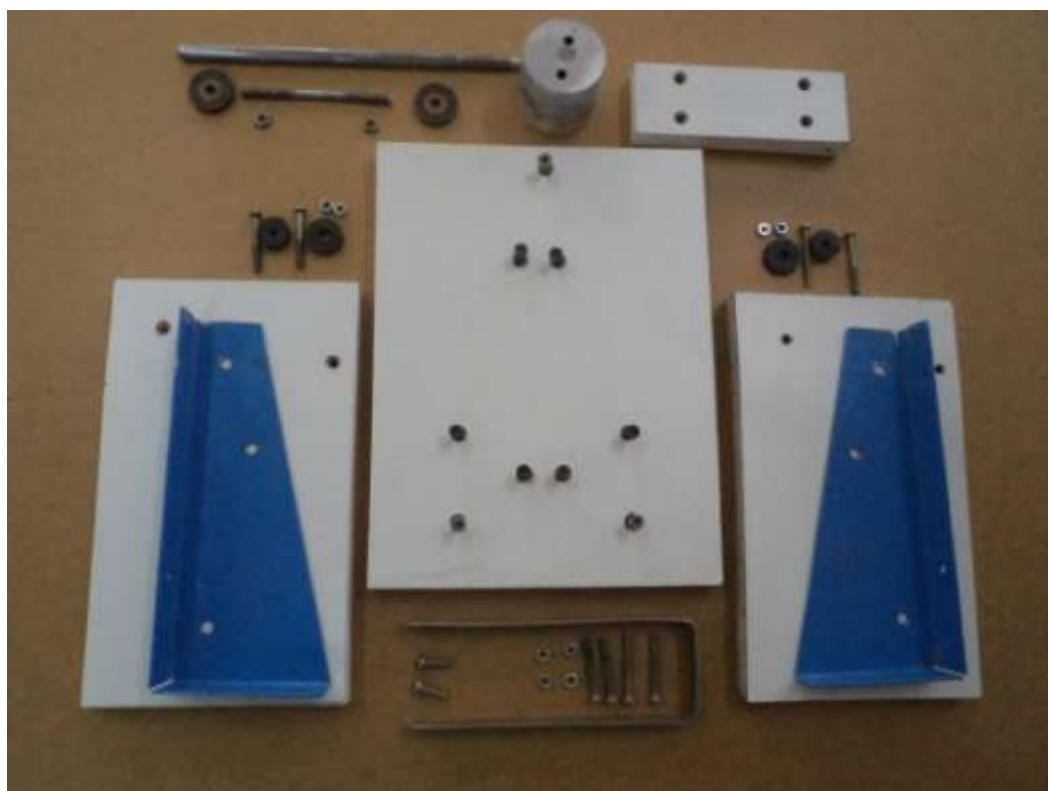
Детали конструктора для зажима и установки пилок в лобзик.
